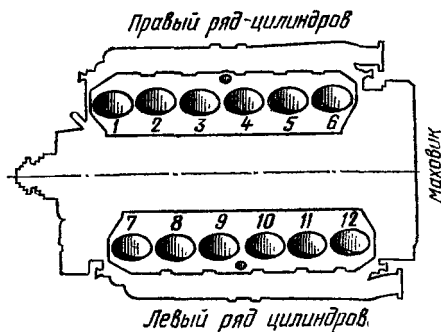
Схема нумерации цилиндров двигателя ЯМЗ-240Б.
